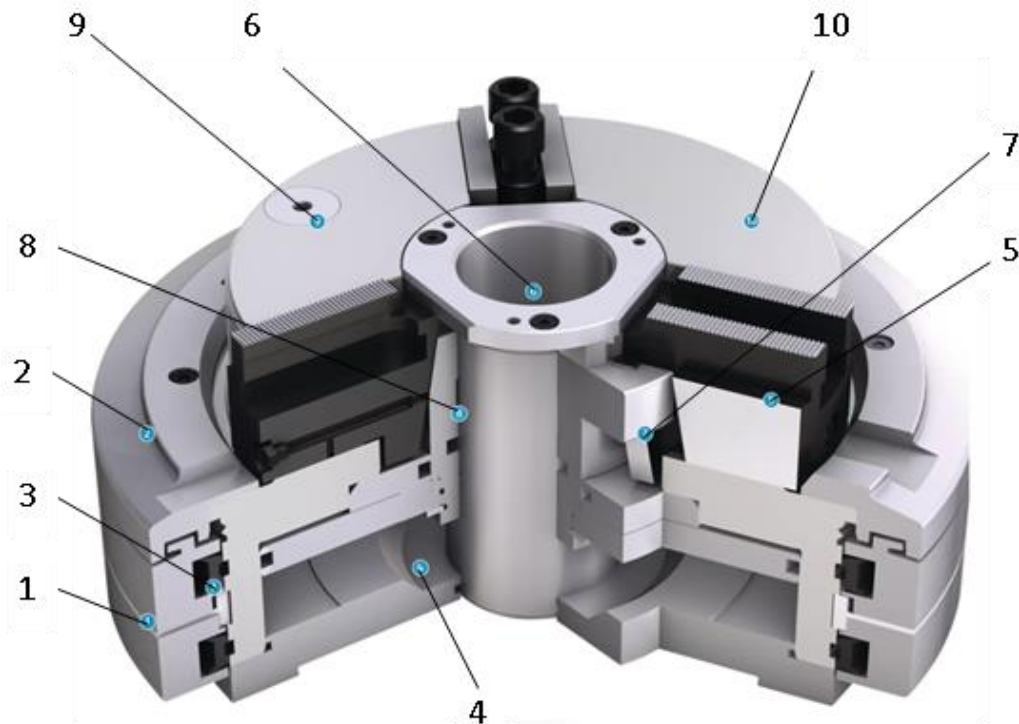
Конструкція пневматичного кулачкового затискного патрона клинового типу серії ROTA TP фірми SCHUNK
